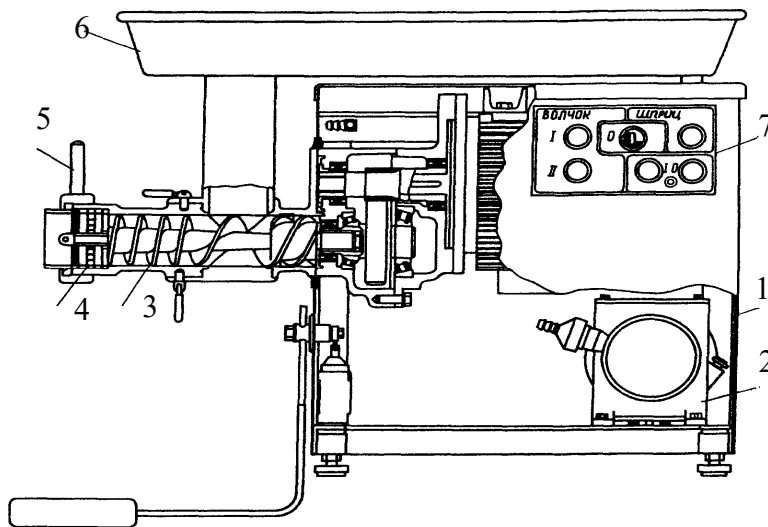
Модульний агрегат ВШ-82: 1 – станина; 2 – привід; 3 – робочий шнек; 4 – механізм, що ріже; 5 – притискний пристрій; 6 – бункер; 7 – пульт керування.
